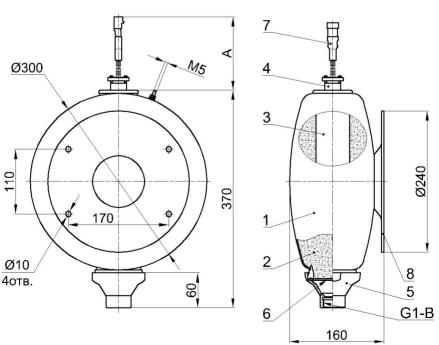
Устройство и габаритные размеры модуля Буран-7КДТ
